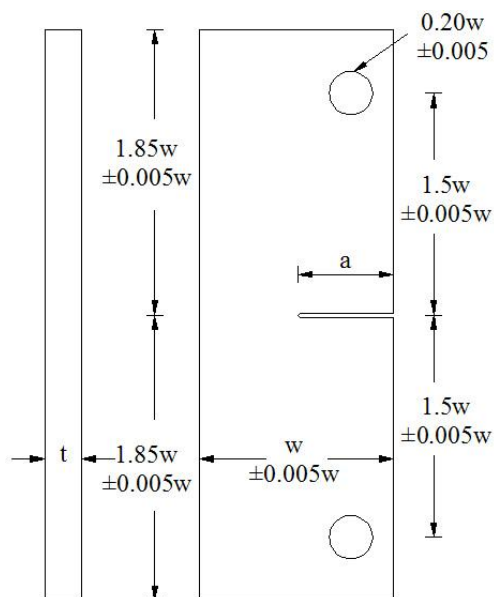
ESE(T) - *Eccentrically-Loaded Single Edge Crack Specimen* utilizado no ensaio da/dN para encontrar as propriedades do material a fadiga.
